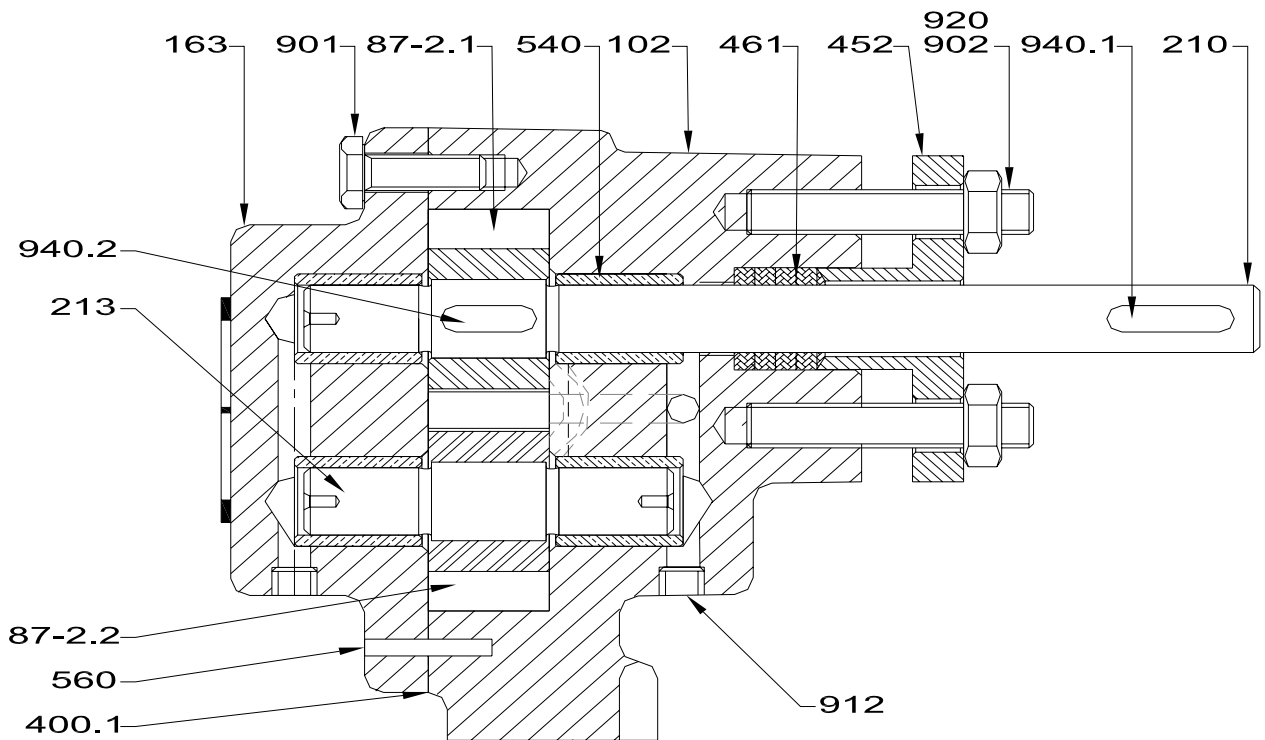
Desenho em Corte bomba FBE 3/8” – 1/2” – 3/4” - 1”com gaxeta
